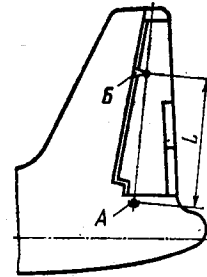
Шарнирный разъем с двумя узлами.
